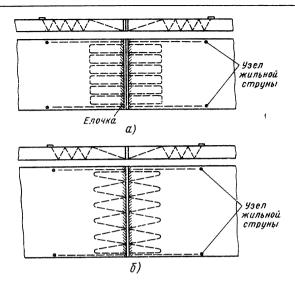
Схема сшивки ремней жильными струнами: a — для работы без натяжного ролика; δ — с натяжным роликом
